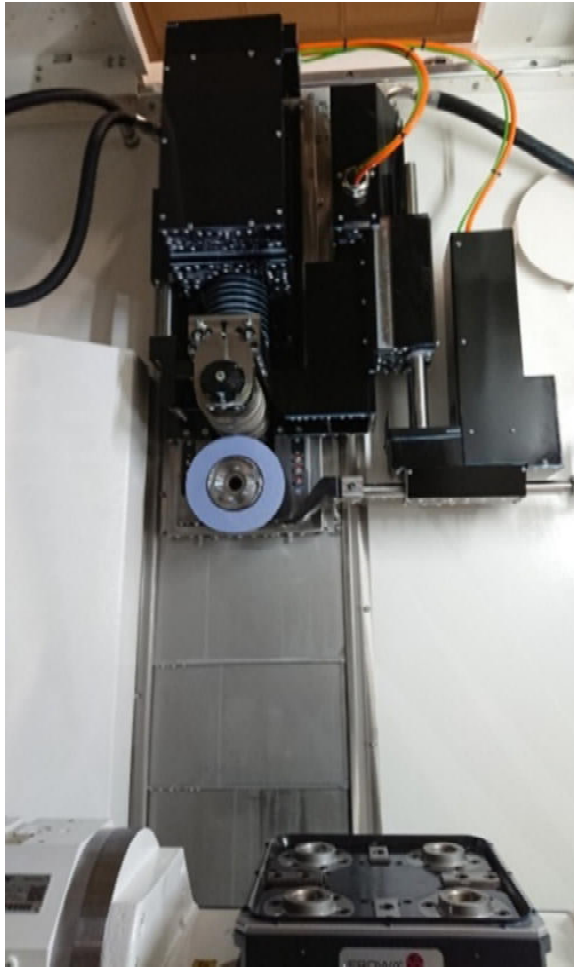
Наклонно-поворотный стол с базовой станцией для установки сменных паллет с приспособлением
